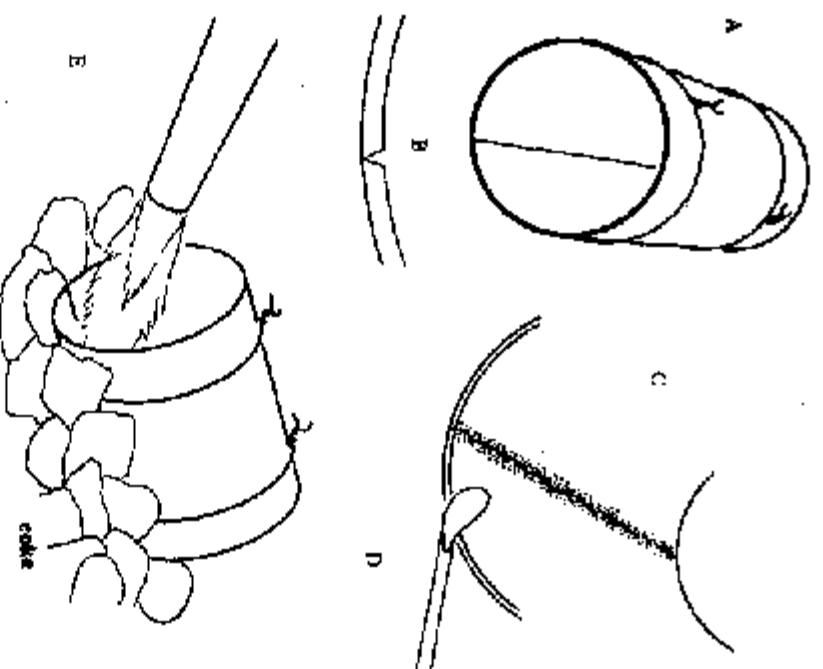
Para aplicar soldadura fuerte a una unión abierta: (A, B, C, D), se amarra con alambre la pieza; (E) y se le apoya sobre coque.
